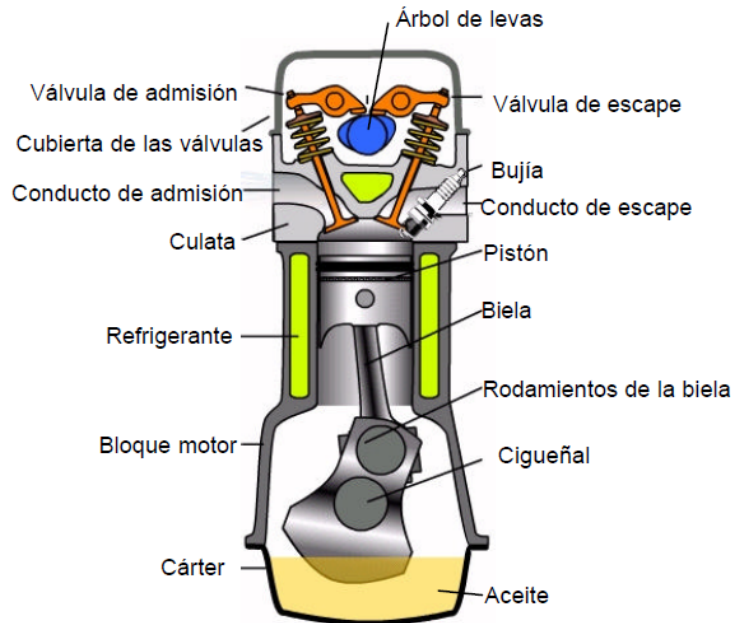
Partes de un motor de combustión interna de gasolina [35]
